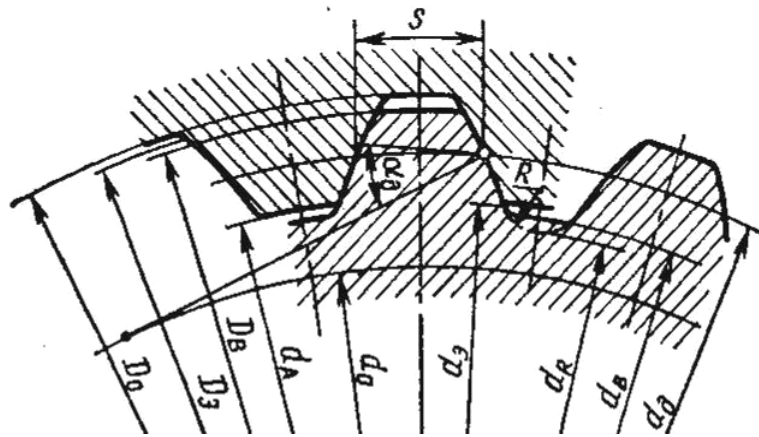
Схема зубчатого евольвентного з'єднання
